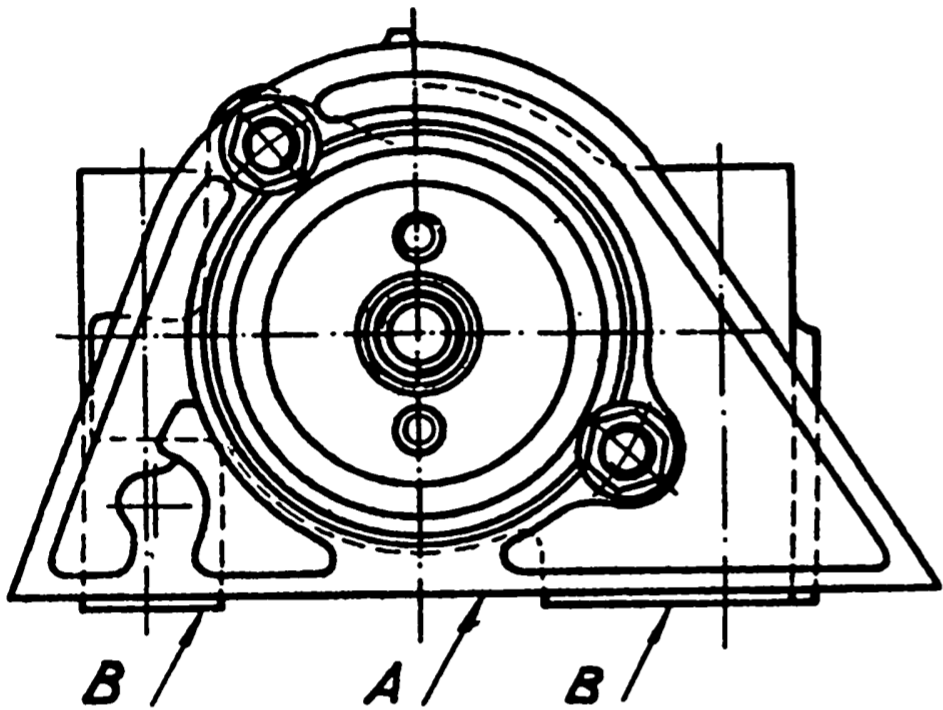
Установка держателя сальника распределительного вала: А - нижняя плоскость держателя; В - нижняя плоскость корпуса подшипников распределительного вала
